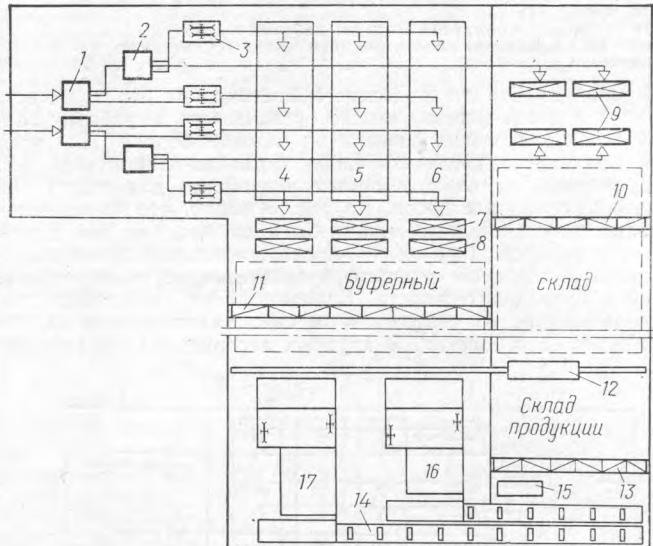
Схема планировки лесопильного завода, выпускающего сырье антисептированные пиломатериалы в пакетах
